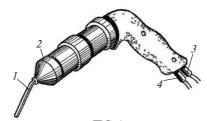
Сварочный пистолет ПС-1 с электрическим подогревом 1— сопло для выхода горячего воздуха, 2— нагревательная воздушная камера; 3— штуцер для подачи сжатого воздуха, 4— электропровод
